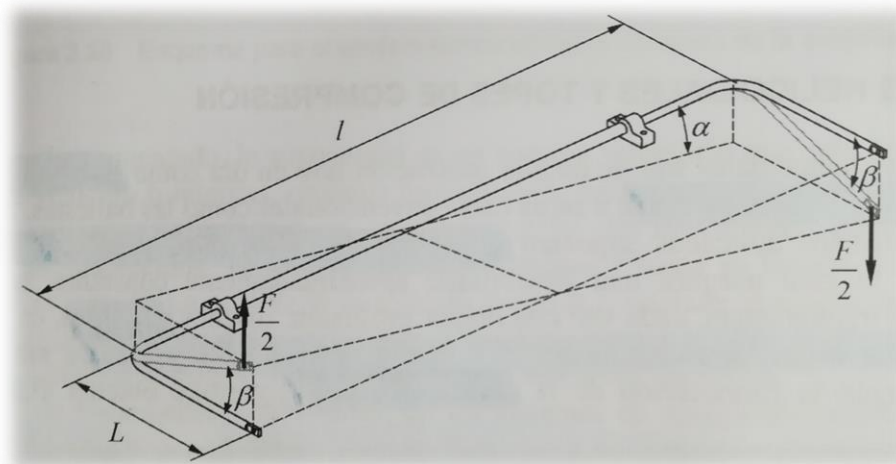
Funcionamiento de la barra estabilizadora. Fuente: Ingeniería del automóvil
